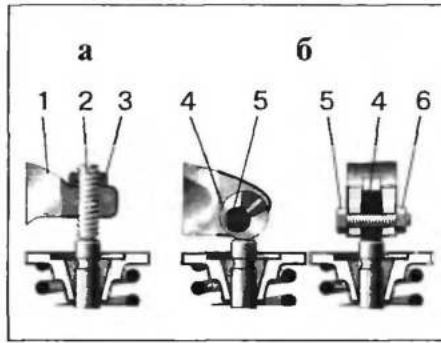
Регулирование зазоров в приводе клапанов коромыслами: а — винтом с контргайкой; б — эксцентриком; 1 — коромысло; 2 — винт; 3 — контргайка; 4 — эксцентрик; 5 — болт; 6 — гайка
